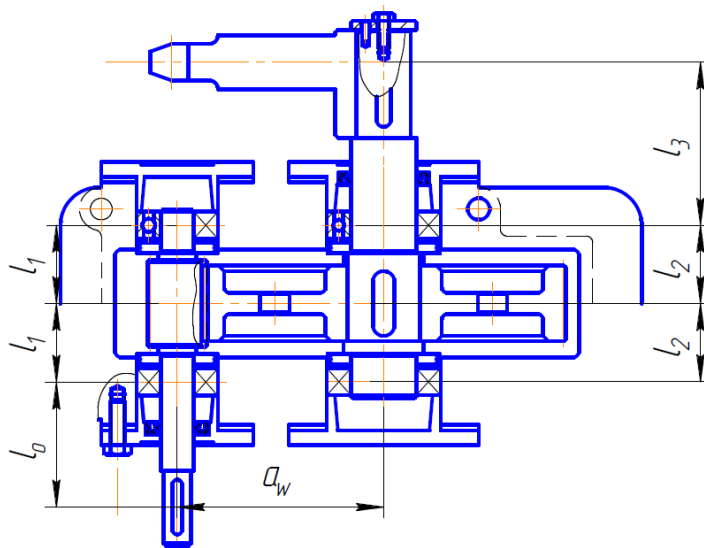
Приклад конструктивної компоновки циліндричного редуктора
